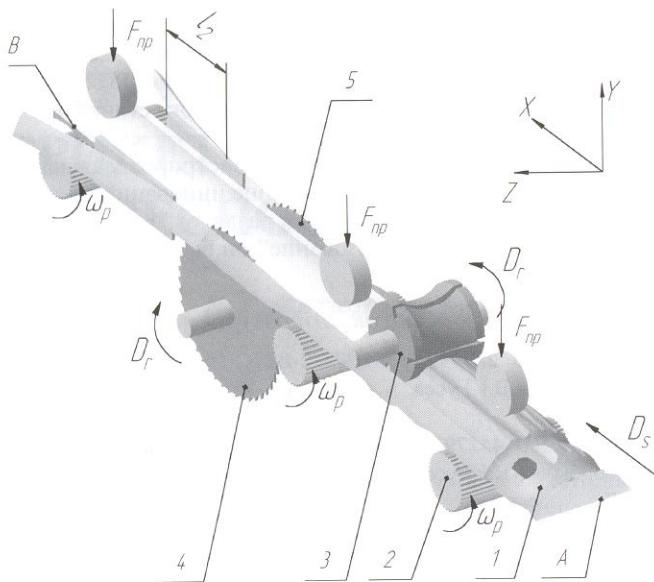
Схема обработки горбыля на станке ПФП-100 с использованием неполного базирования
